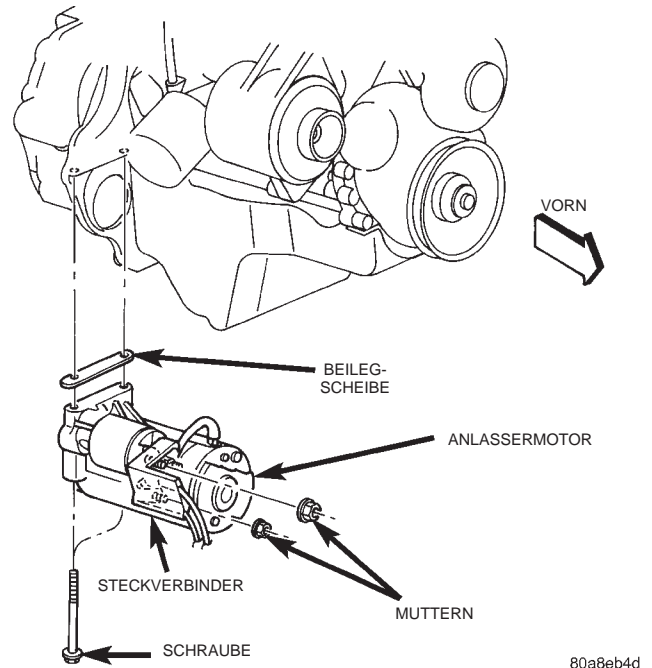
Anlassermotor aus- und einbauen—2.5L-Motor
